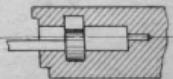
Станок для фрезеровки гнезд для ремонтуара.
